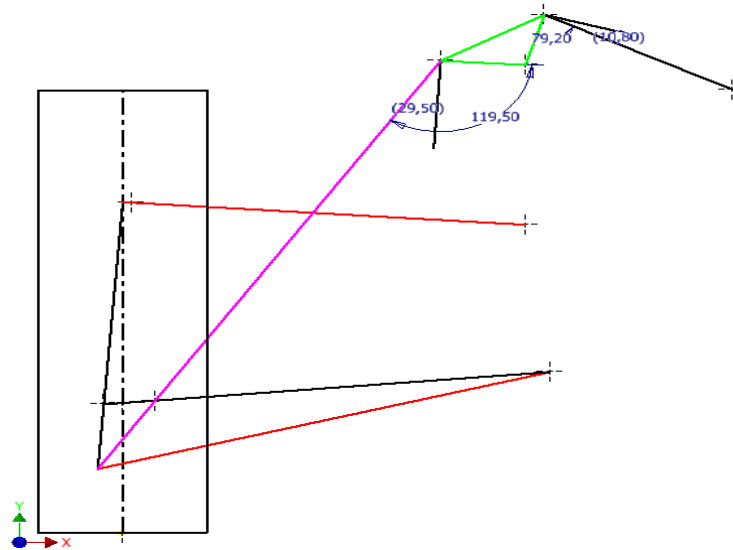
Proyección en un mismo Plano de la Geometría de la Suspensión Eje Delantero
